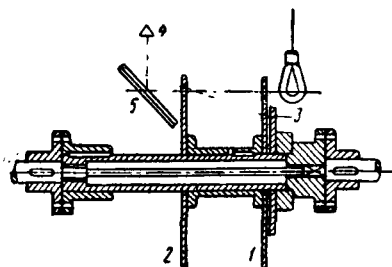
Схема установки проволочного датчика для измерения деформации вала
